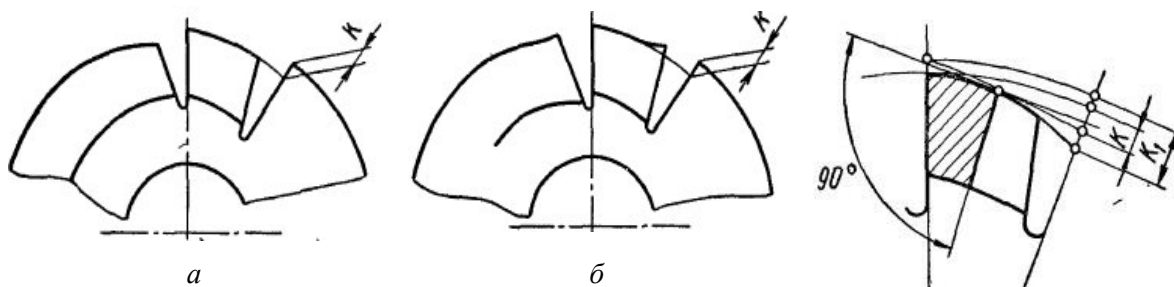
Правильный (а) и неправильный седлообразный (б) спады затылка у фрез
